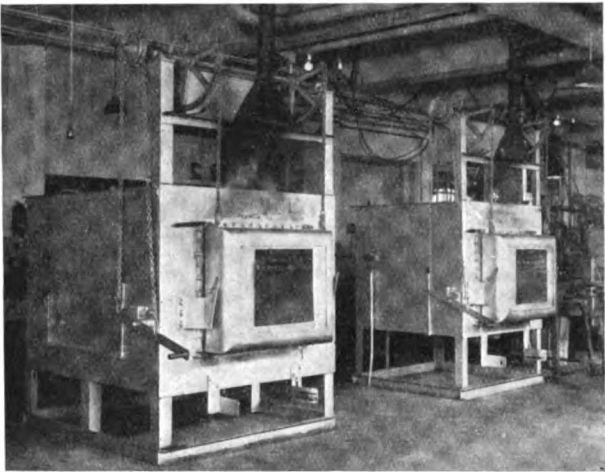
Einsatzöfen für Fertigungsteile (rechts) und für Werkzeugteile (links).
